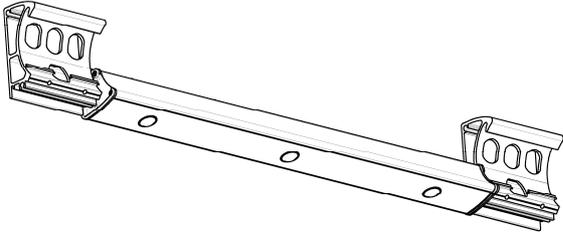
Sondervariante Dachsparrenbefestigung vertauscht mit Dachsparrenhalter ohne Montageplatte
